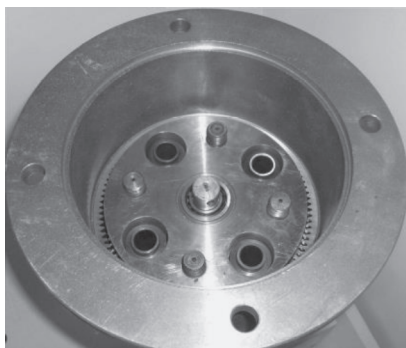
Вариант планетарной передачи с внутренними зацеплениями колес и роликовым механизмом снятия движения с сателлитов.
